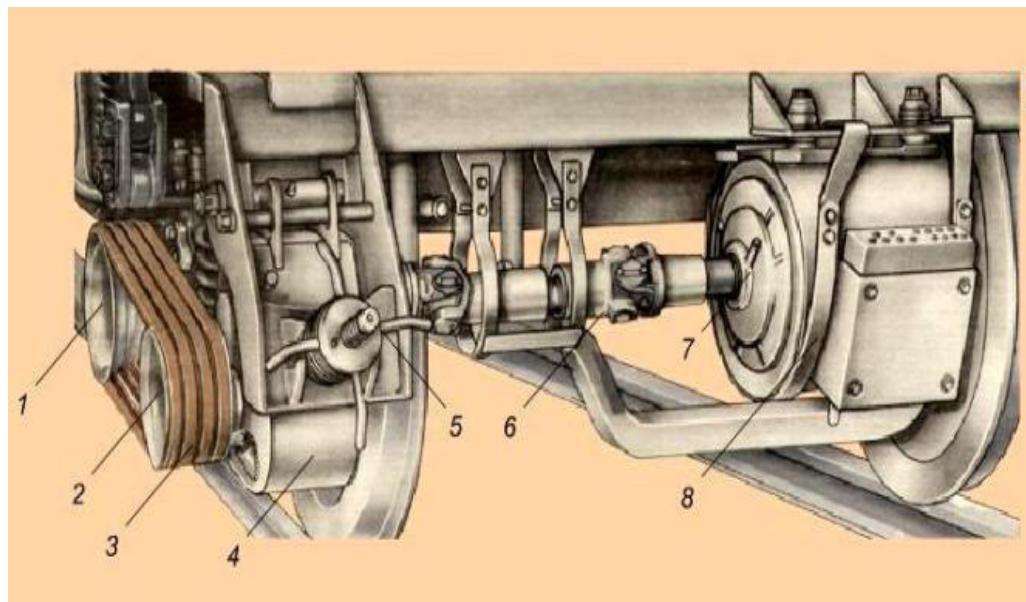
Расположение текстропно-редукторно-карданного привода
